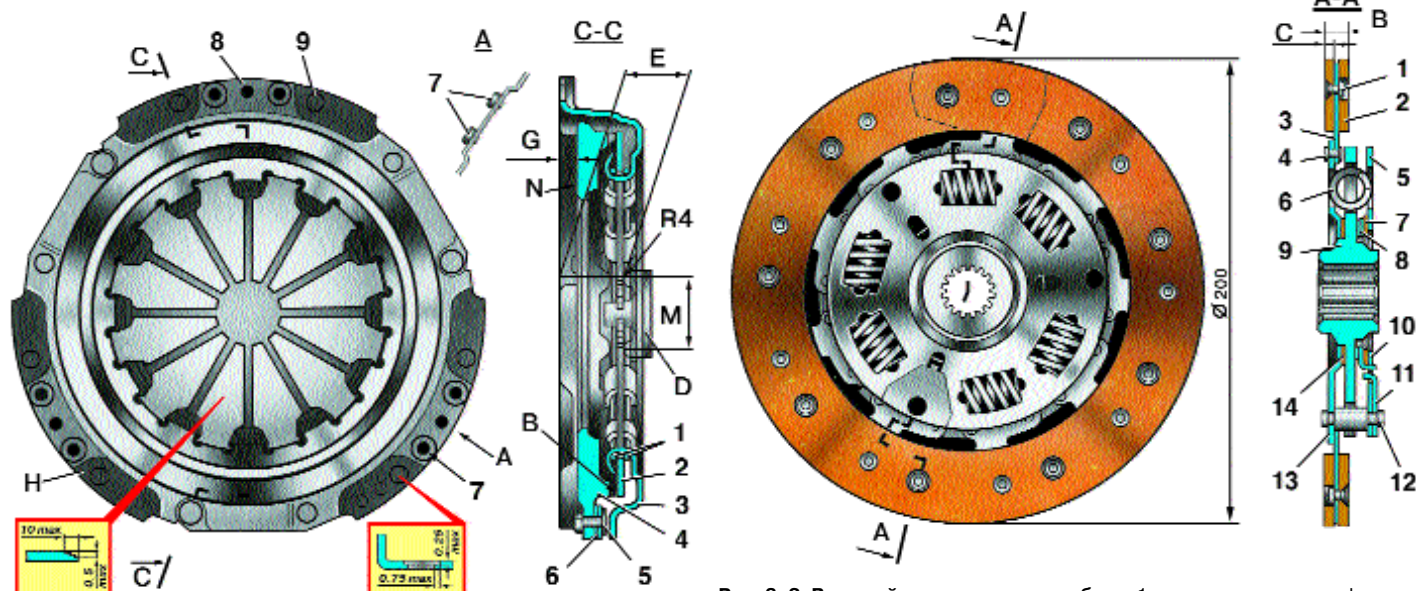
Нажимной диск сцепления с кожухом в сборе: 1 – опорные кольца; 2 – нажимная диафрагменная пружина; 3 – кожух сцепления; 4 – нажимной диск; 5 – заклепка; 6 – соединительная пластина; 7 – балансировочные грузики; 8 – отверстия под установочные штифты; 9 – крепежные отверстия
